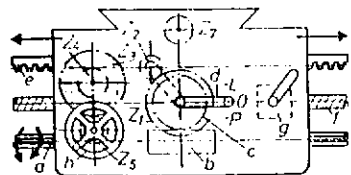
Mecanismo de engranajes del carro principal o de bancada (muy simplificado). a) Husillo de cilindrar (provisto de ranura longitudinal); b) tornillo sin fin que es desplazable sobre el husillo de cilindrar en sentido longitudinal mediante ranura y chaveta; con objeto de que el tornillo pueda seguir el movimiento longitudinal, va soportado en una carcasa, junto a la caja de mecanismos; c) rueda helicoidal; d) palanca de maniobra, o de embrague; e) cremallera; f) husillo principal o de cilindrar; g) tuerca matriz; h) volante de maniobra para producir a mano el avance longitudinal a través de las ruedas dentadas Z_1, Z_2, Z_3 .
